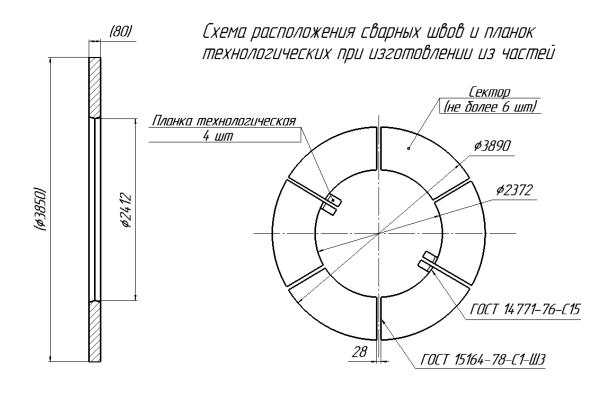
Рабочий чертёж для сборки основного диска мельницывентилятора, швы сварные
